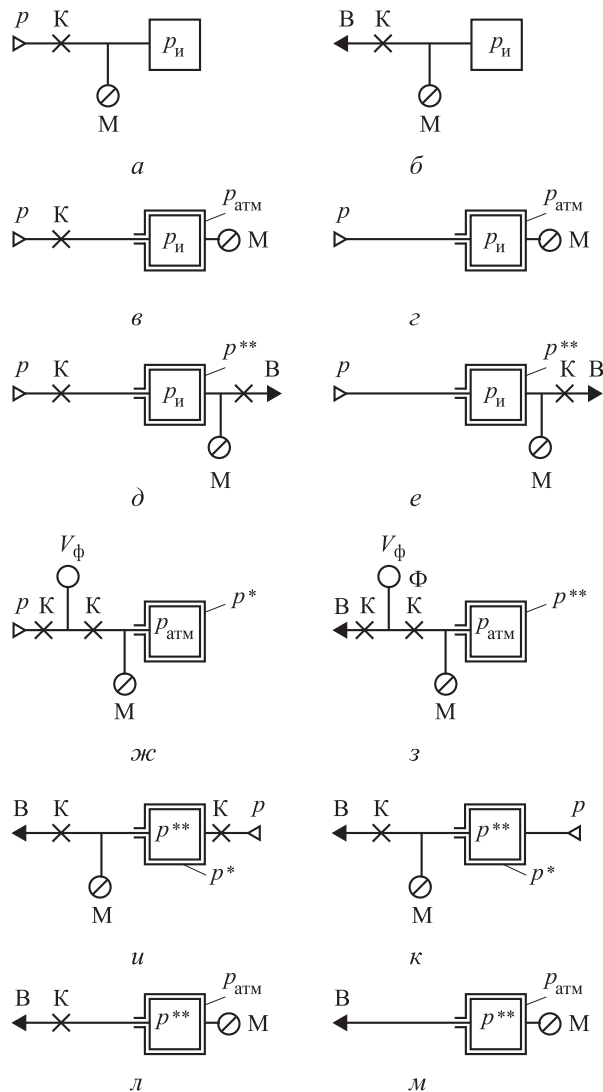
Схема испытания изделий при бескамерном (а, б) и камерном (в–м) способах контроля: p — давление; К — клапан; М — регистрирующий прибор; В — вакуум; Ф — камера предварительного сжатия (форкамера); V_Φ — объем форкамеры
